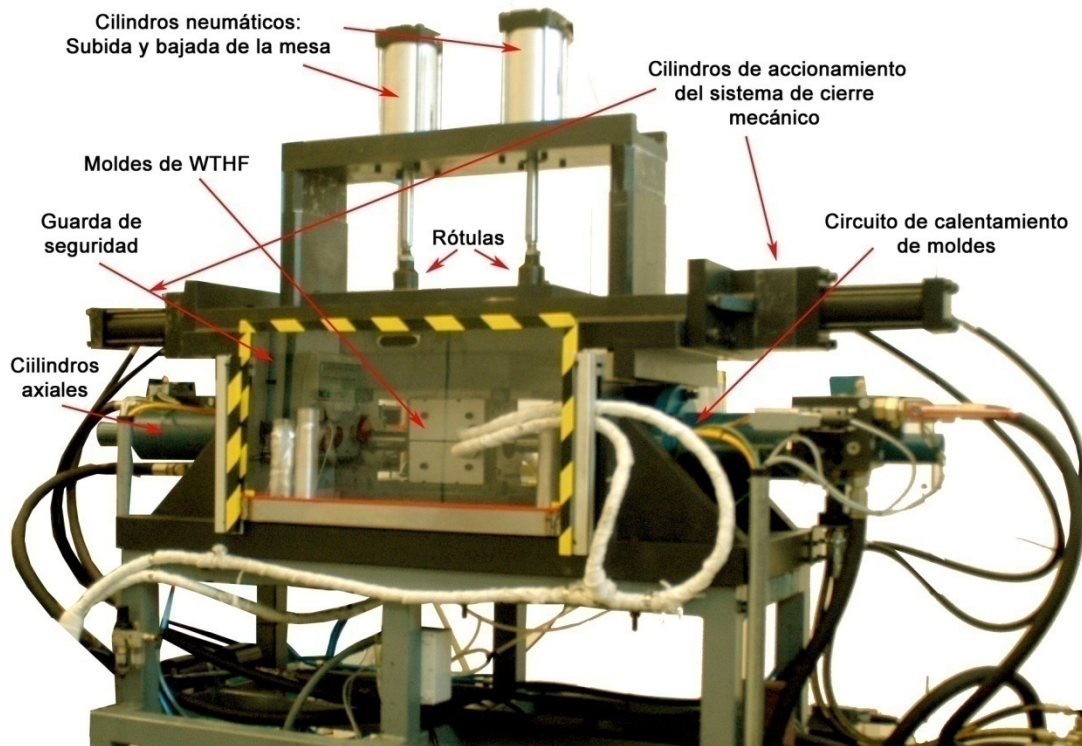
Instalación piloto para hidroconformado de tubo en caliente
